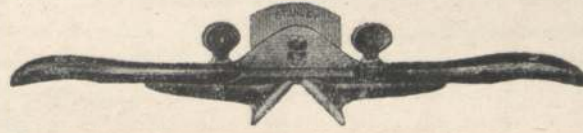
Schabhobel „Kantenglätter“ mit Stellvorrichtung zum Hobeln der Kanten.
